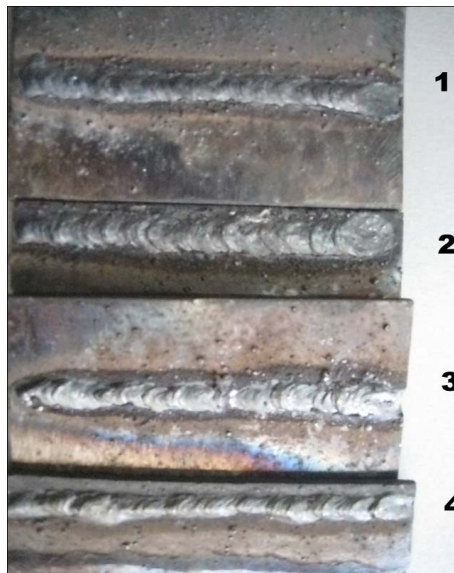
Внешний вид валиков, выполненных ручной дуговой сваркой:
